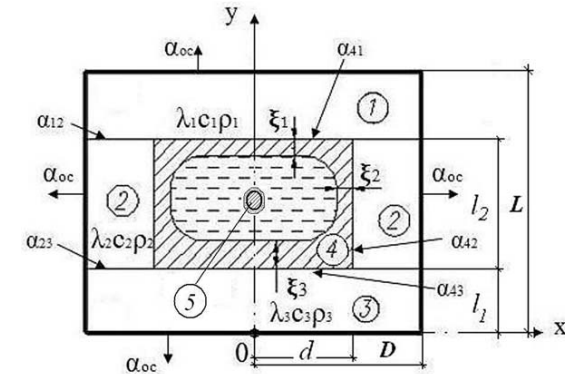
Схема к расчету теплообмена при литье отливки в кокиль: d — половина толщины отливки; D — половина ширины конструкции кокиля по наружному обмеру; l_1 — толщина нижней плиты кокиля; l_2 — высота отливки; L — высота конструкции кокиля по наружному обмеру; ξ_1, ξ_2, ξ_3 — толщина затвердевшего металла на рабочих поверхностях элементов кокиля
